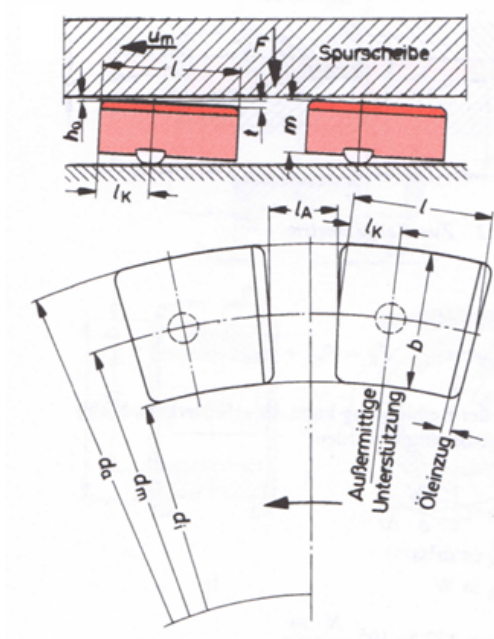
Axial Kippsegmentlager für eine Drehrichtung [20]
